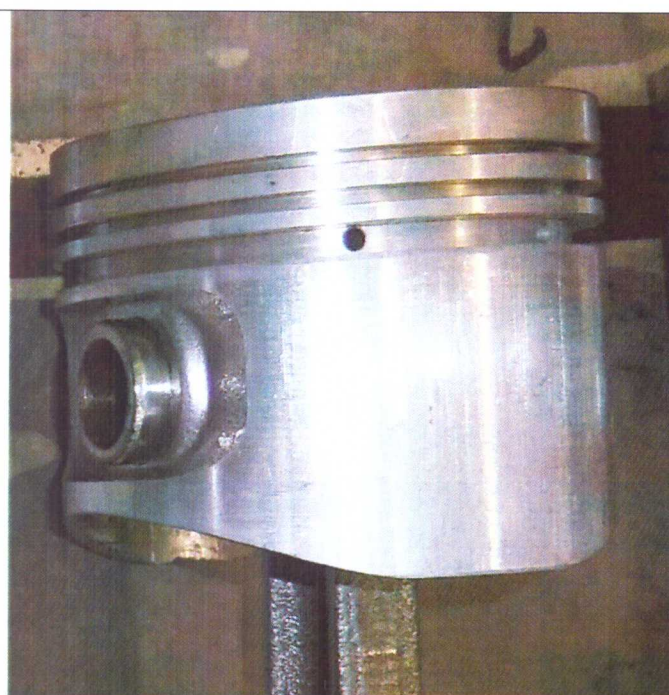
Внешний вид боковой поверхности поршня третьего цилиндра по окончании длительных испытаний двигателя при работе на базовом масле Castrol EDGE с добавкой нанокompозита Amortect PROOF
